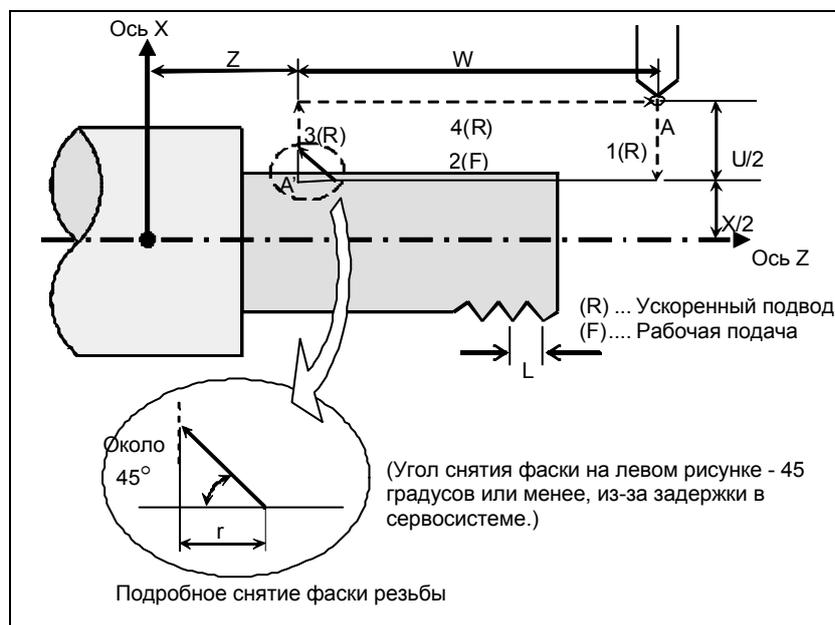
(a) Нарезание цилиндрической резьбы
